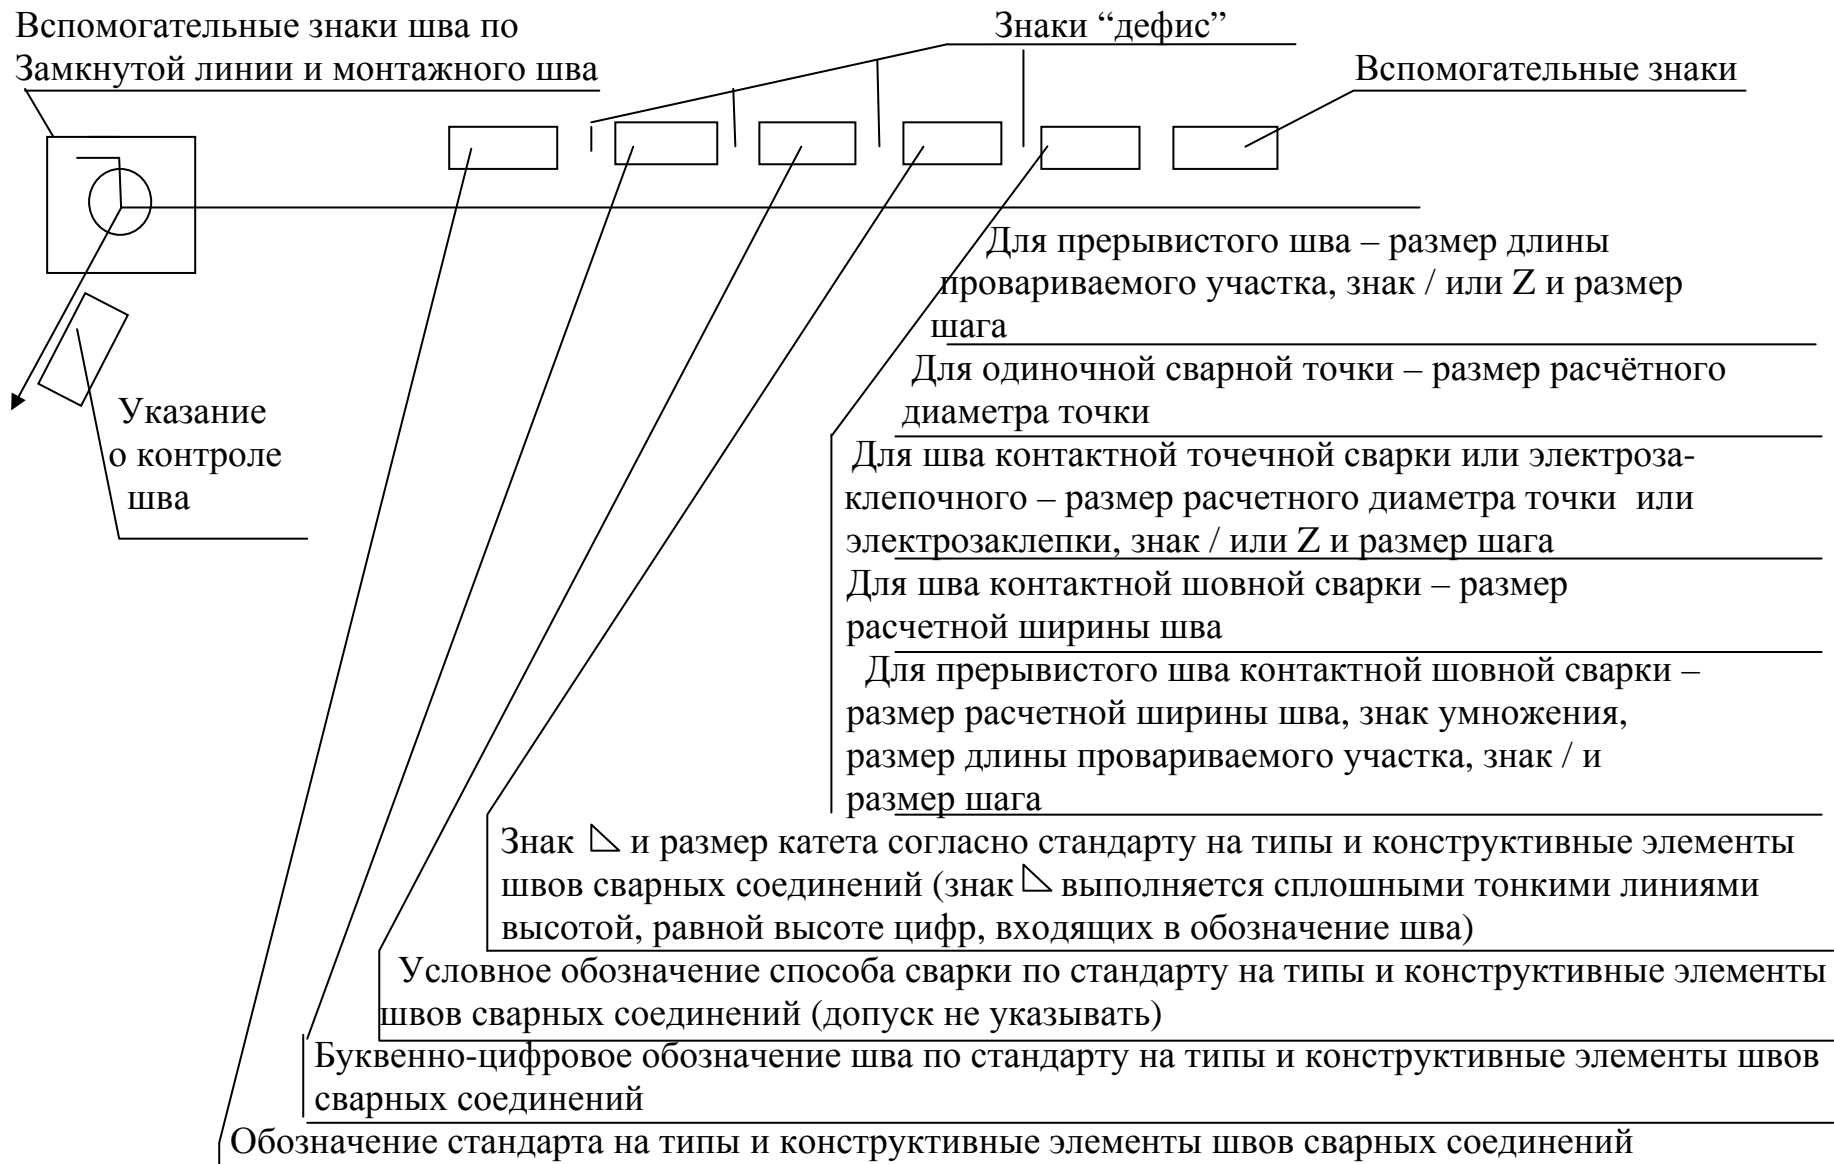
Структура условного обозначения стандартного шва или одиночной точки
